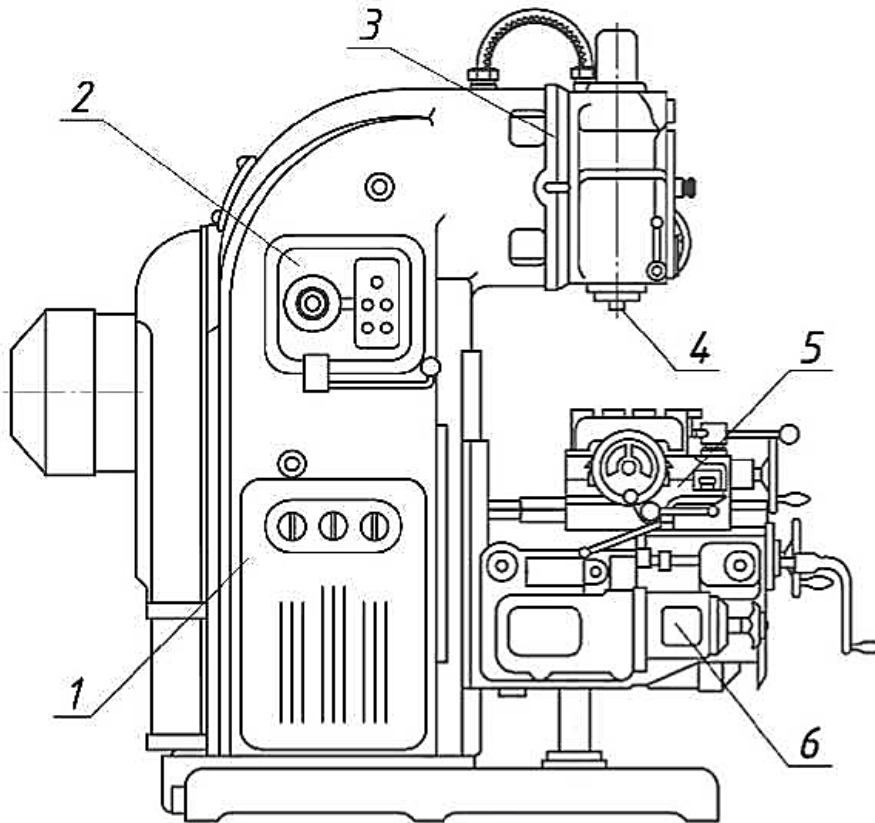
Загальний вигляд вертикально-фрезерного верстата
